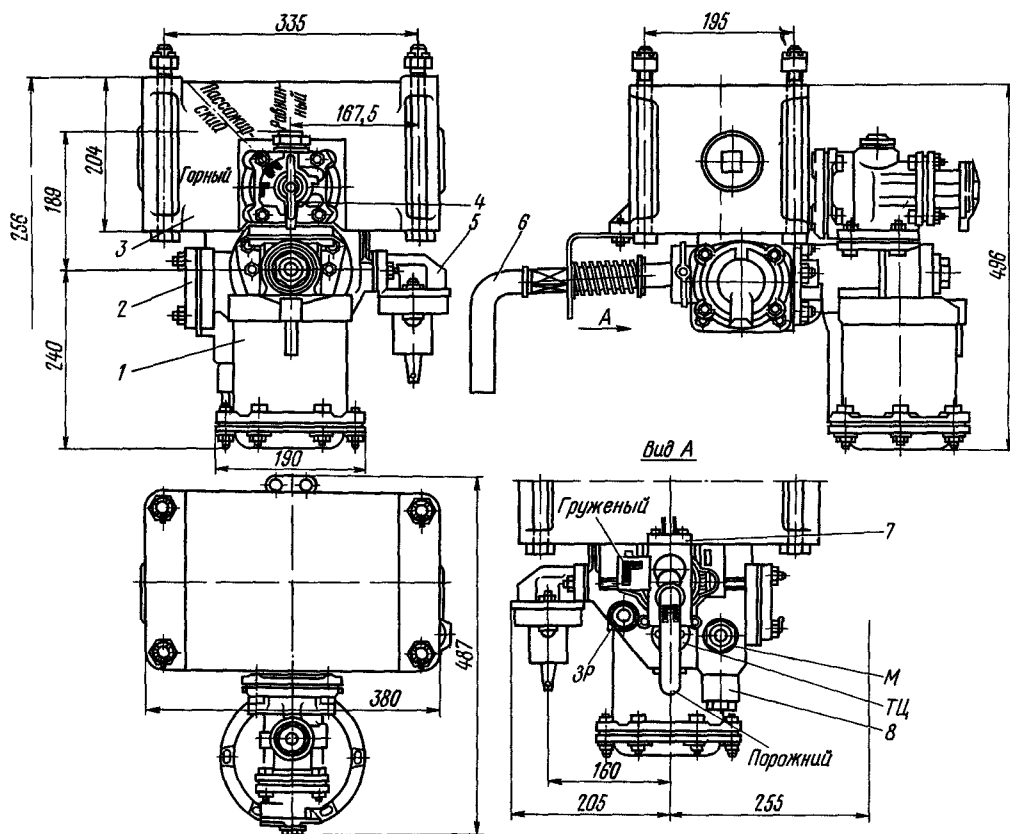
Воздухораспределитель № 135 и двухкамерный резервуар № 145
